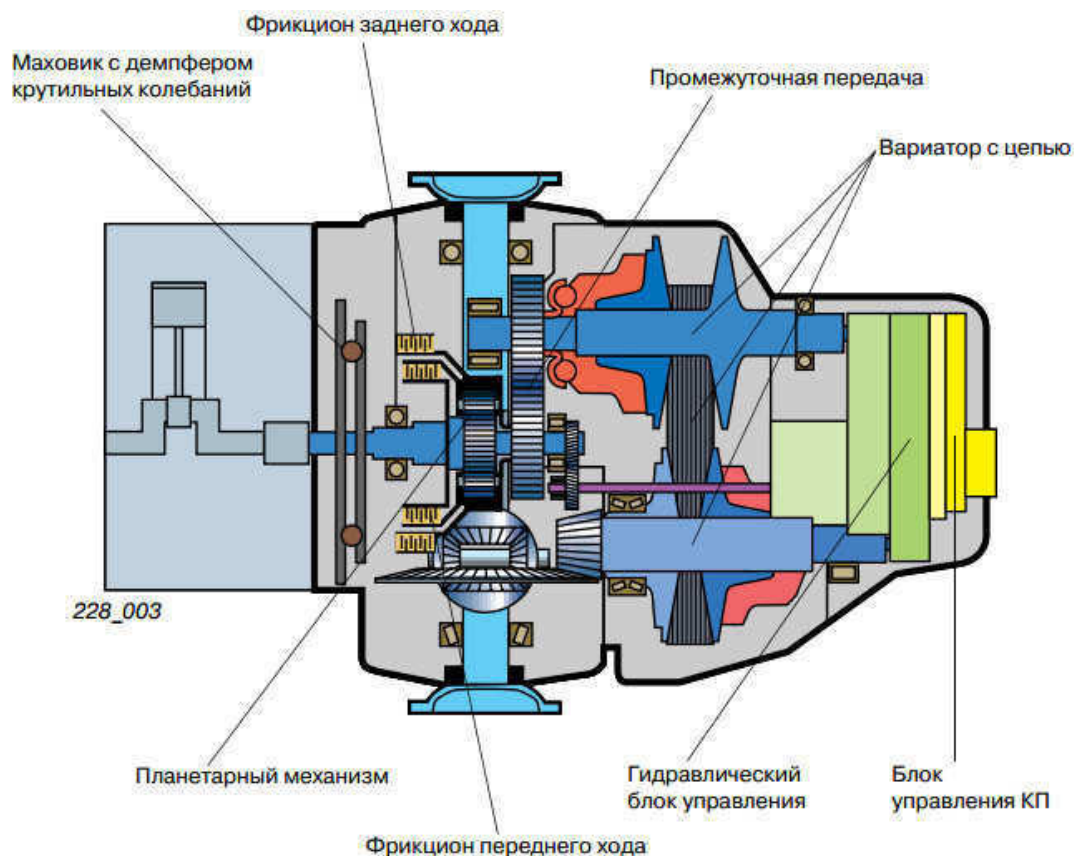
Общий вид коробки передач типа Multitronic 01J
